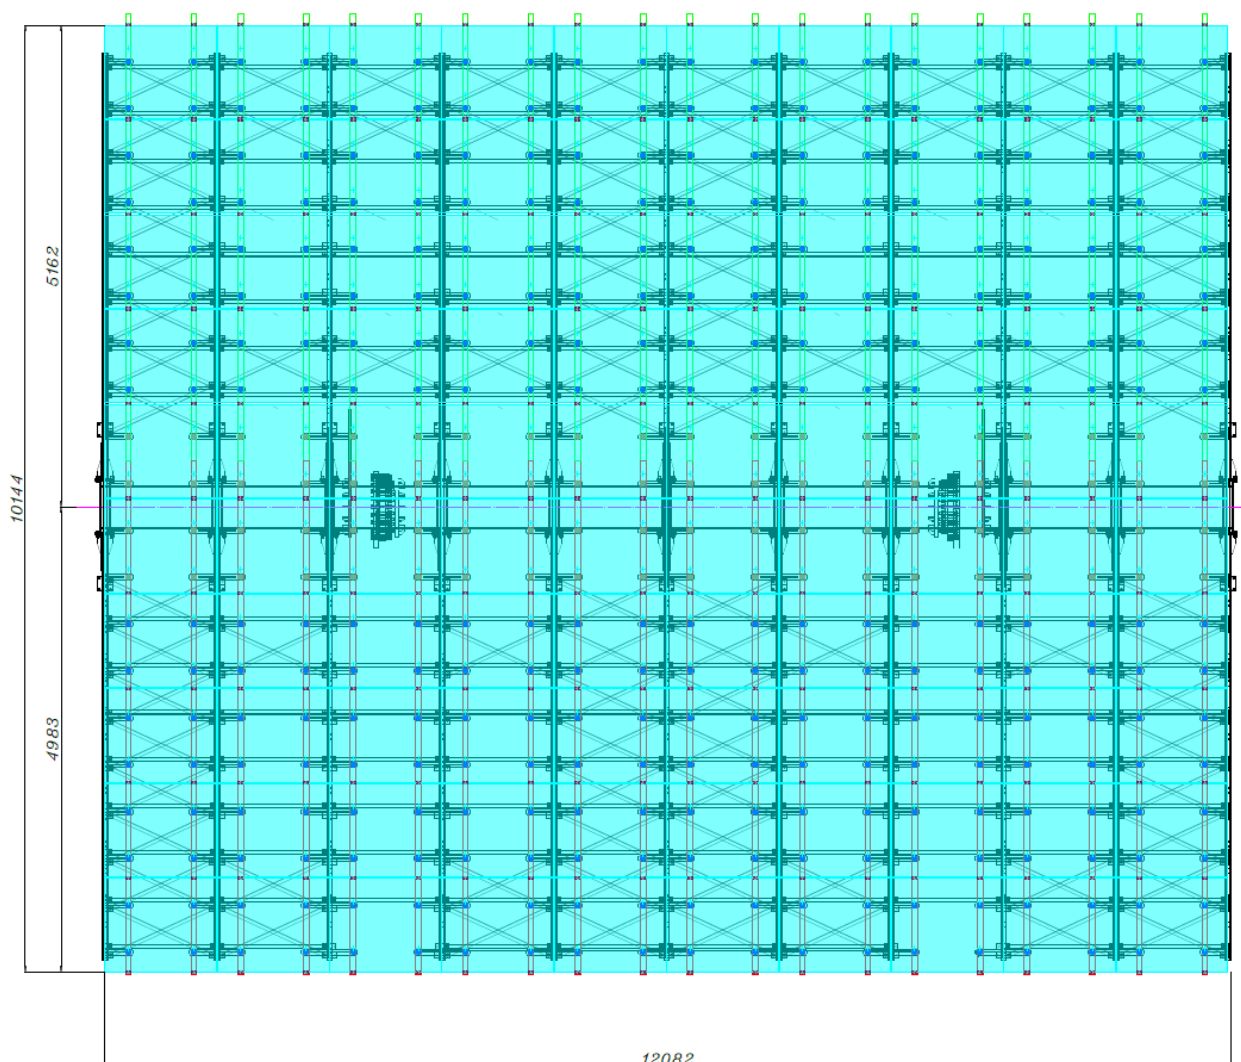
Vista della vela dell'eliostato a montaggio degli specchi piani terminato
